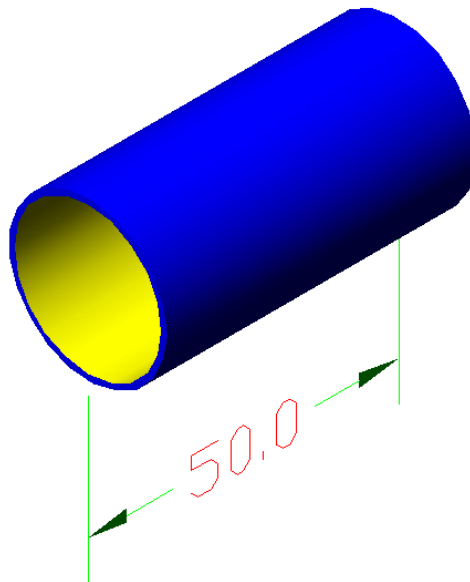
Probeta de Tubo galvanizado por inmersión.
